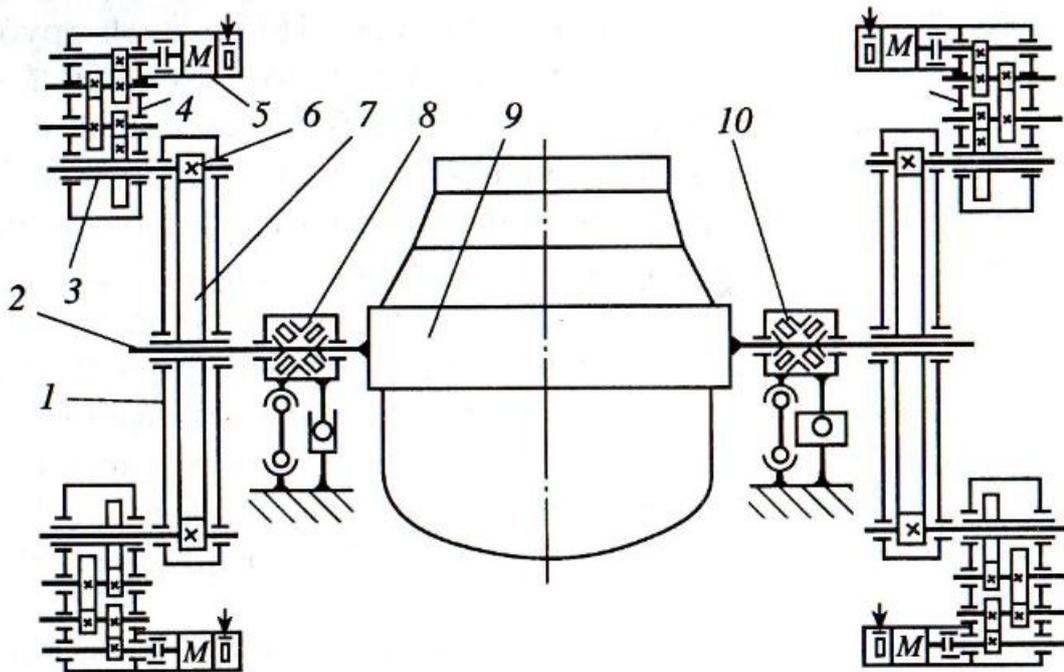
Кинематическая схема навесного многодвигательного привода конвертора: 1 – тихоходные редукторы, 2 – цапфа, 3 - , 4 – быстроходный трехступенчатый редуктор, 5 – электродвигатель, 6 – вал-шестерня, 7 – зубчатое колесо, 8 – плавающая опора, 9 – опорное кольцо, 10 – плавающая опора.
